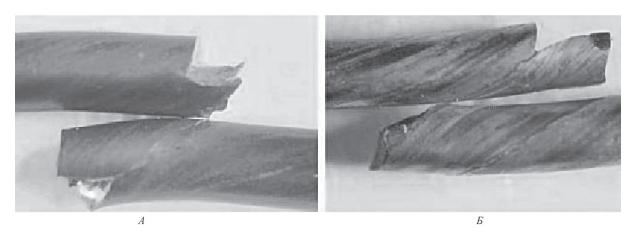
Образцы проволоки с пониженными значениями числа скручиваний до разрушения и со ступенчатым изломом
